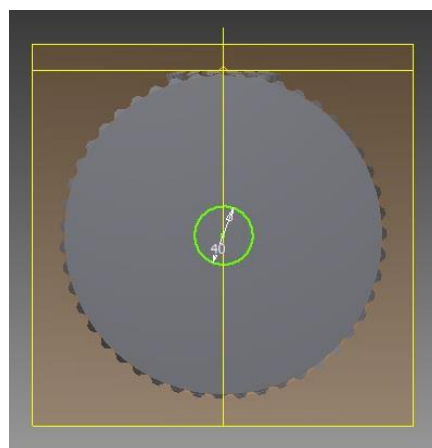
DETALLE BOCETO PERFORACIÓN ENGRANAJE 2
